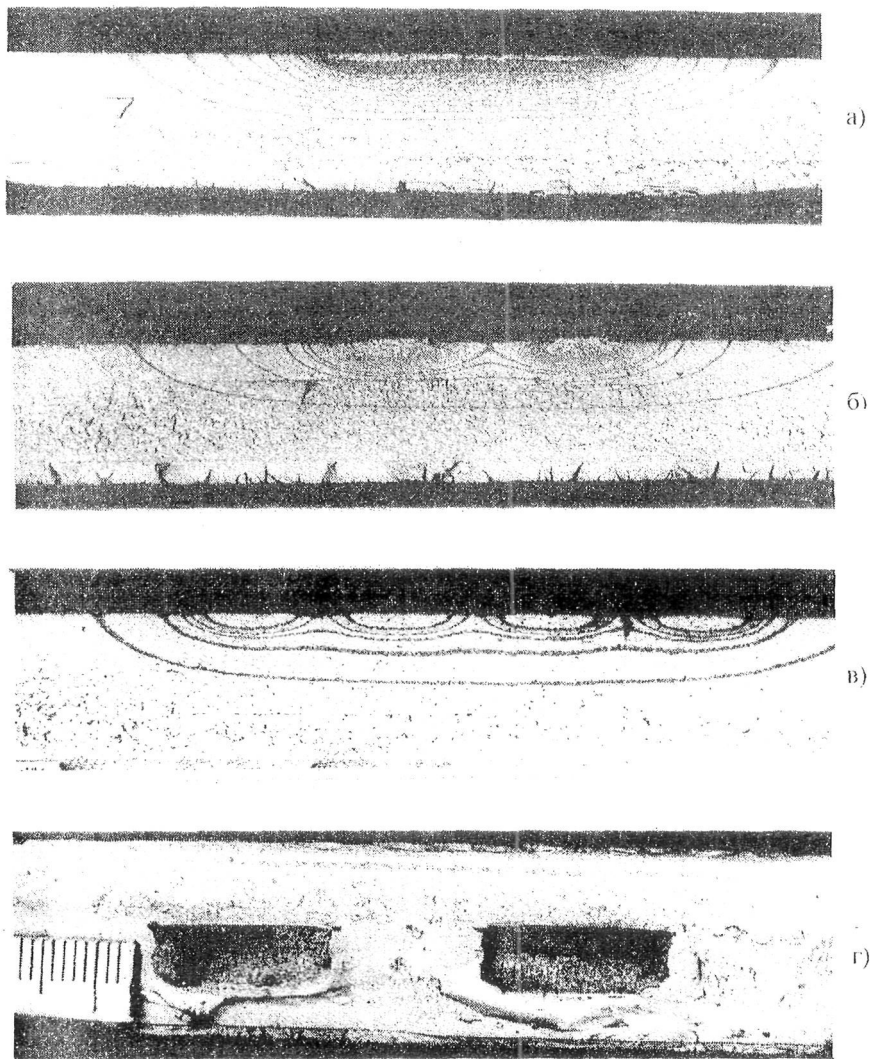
Изломы образцов с внутренними дефектами
